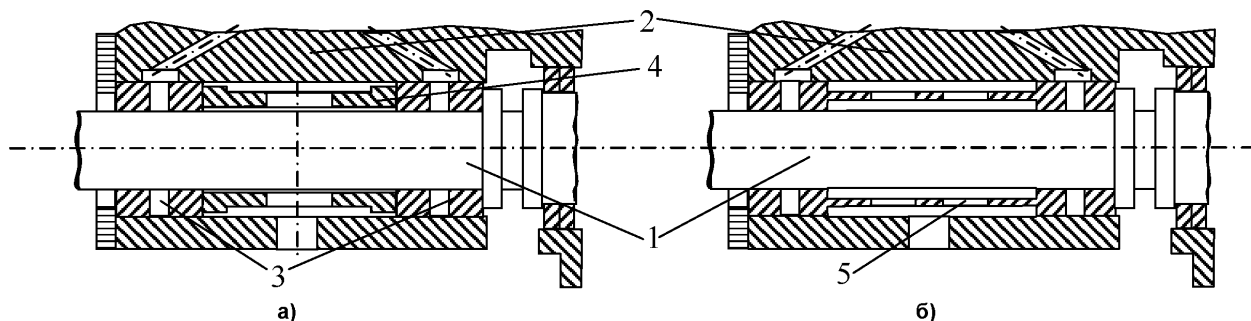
Конструкции подшипниковых узлов роторов турбокомпрессоров с ПВ втулками – а, с ПН моновтулкой – б: 1 – ротор, 2 – корпус подшипников, 3 – ПВ втулки, 4 – дистанционная втулка, 5 – ПН моновтулка
